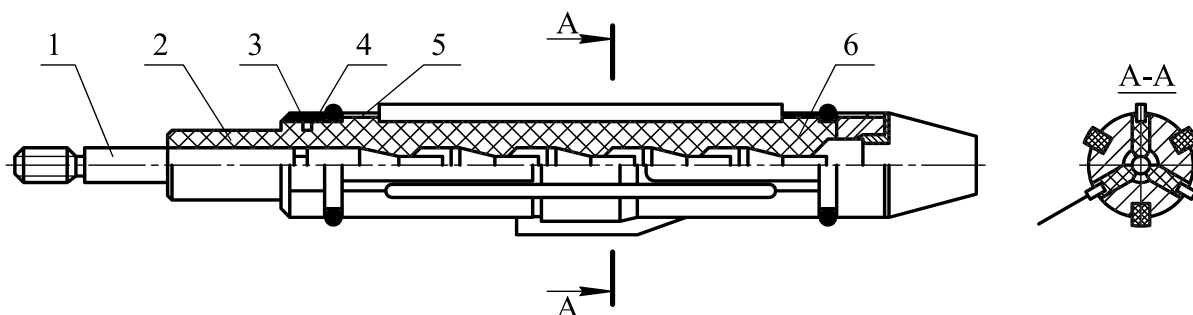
Хон–инструмент. 1 – разжимной конус; 2 – корпус хона; 3 – резиновое кольцо; 4 – держатели брусков; 5 – направляющие; 6 – пружина.
